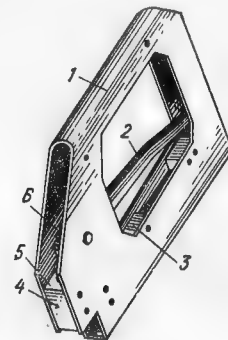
1 — корпус; 2 — рычаг спусковой; 3 — механизм ударный; 4 — пуансон; 5 — матрица; 6 — пружина возвратная
